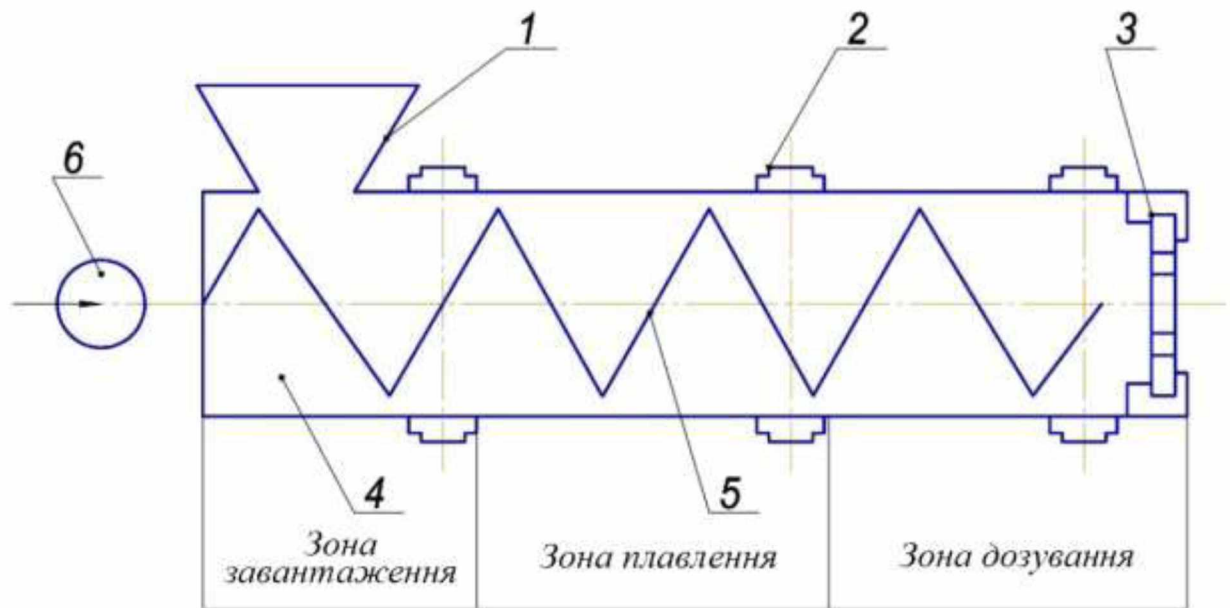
Зони шнекової камери прес-екструдера: 1 - завантажувальний пристрій; 2 - фланцеві з'єднання; 3 - формуюча головка; 4 - корпус преса; 5 - шнек; 6 - привід пресує шнека
